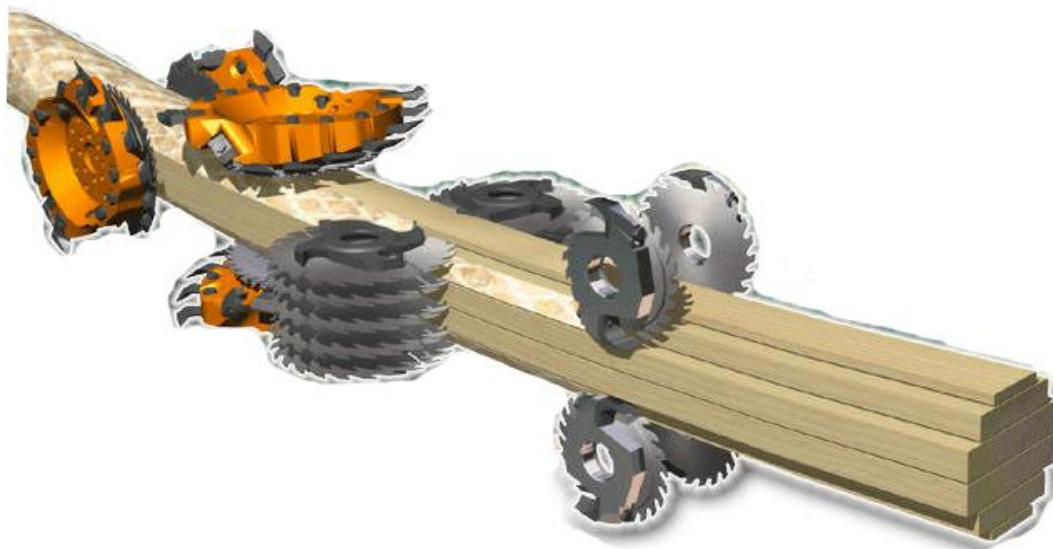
Принцип работы фрезерно-профилирующего оборудования
